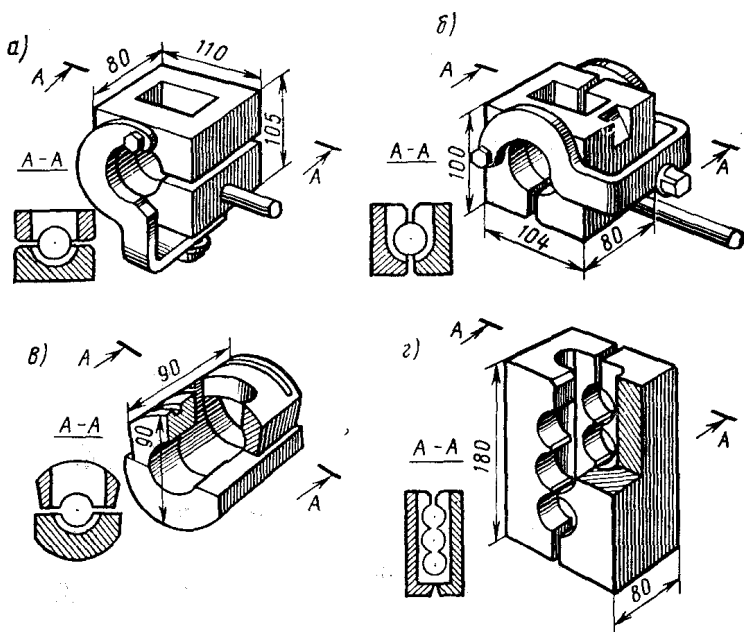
Инвентарные составные медные формы с канавками для сварки стыковых соединений горизонтальных стержней:
